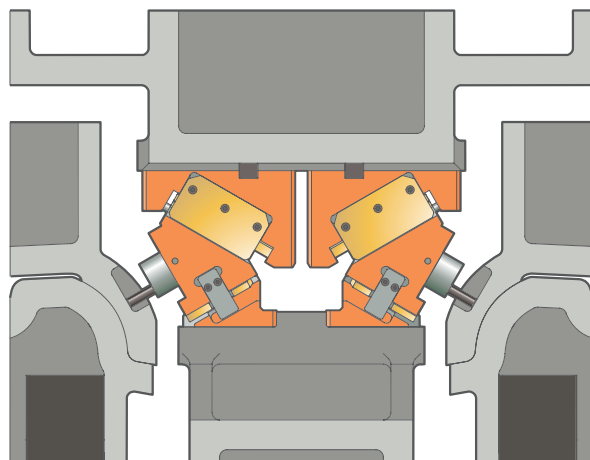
Schieber Rücken an Rücken in Werkzeug mit Doppelfertigung
